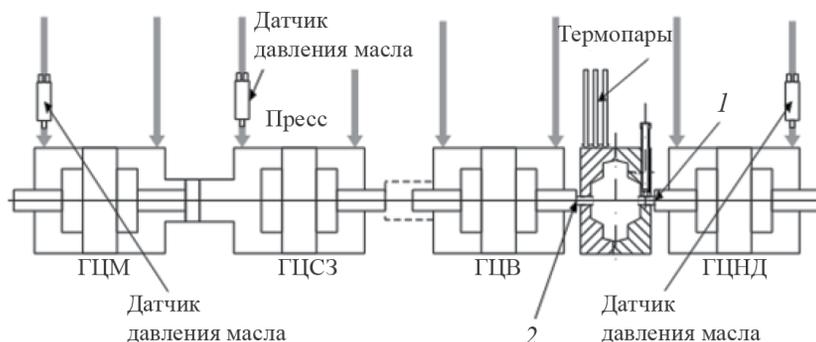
Схема расположения датчиков: ГЦМ — гидроцилиндр мультипликатора; ГЦЗ3 — гидроцилиндр силового замыкания; ГЦВ — гидроцилиндр встроенный; ГЦНД — гидроцилиндр наложения давления; 1 — правый прессующий плунжер; 2 — левый прессующий плунжер.
